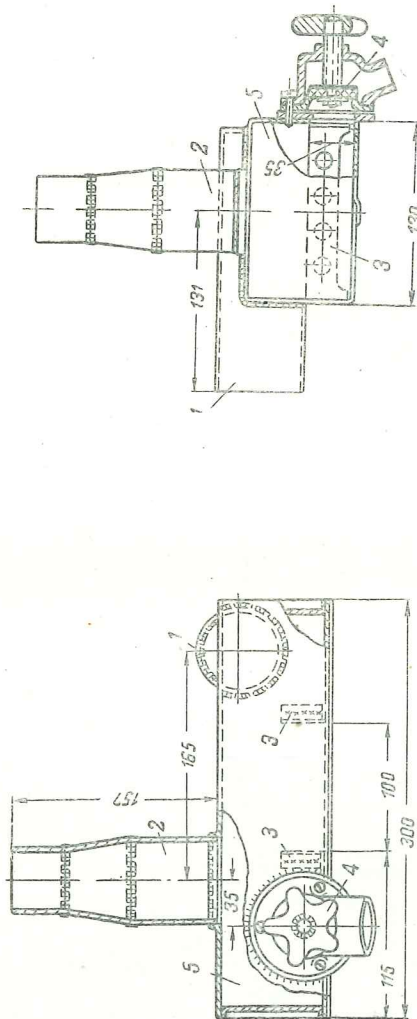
Схема отстойника установки ЗИС для автомобиля ЗИС-21
